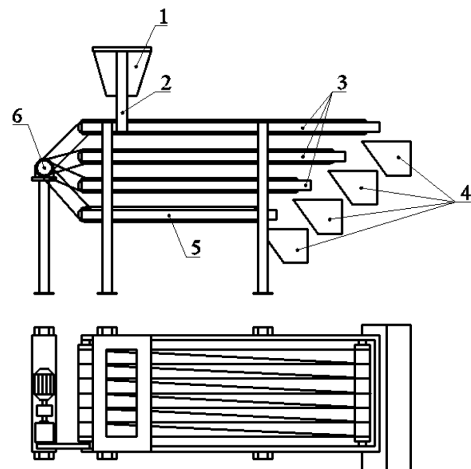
Грохот с канатным движущимся полем: 1 – загрузочное устройство; 2 – рама; 3 – канатный блок; 4 – приемный бункер; 5 – конвейерный блок; 6 – привод
